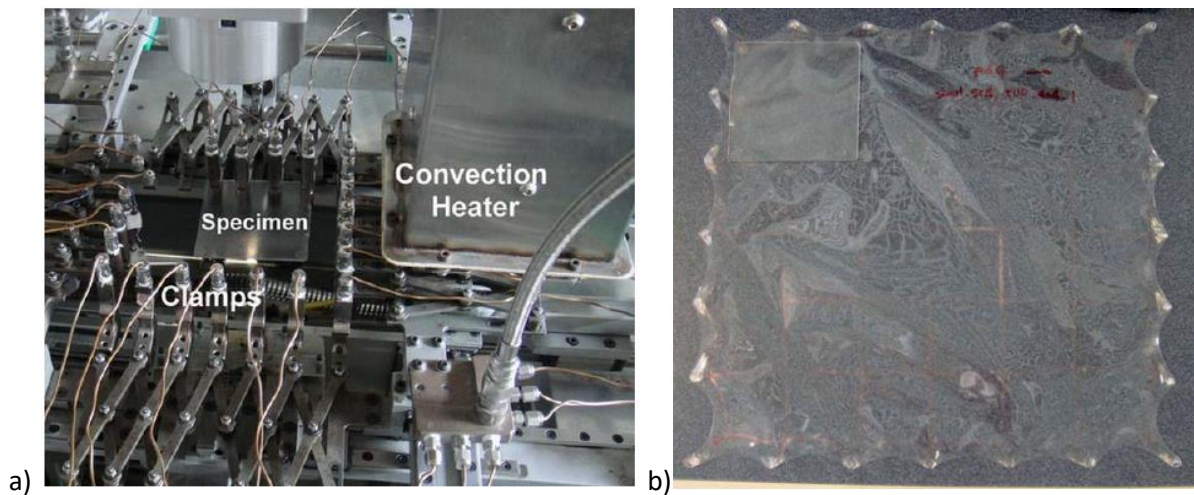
Machine de traction bi-axiale Belfast, b) éprouvette initiale et déformée [42]
